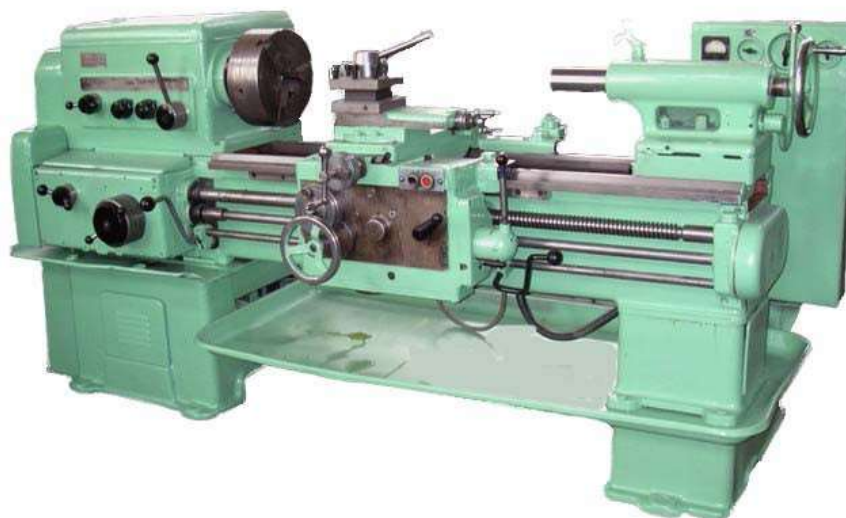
Внешний вид токарно-винторезного станка 1К62 (завод «Красный пролетарий»)
